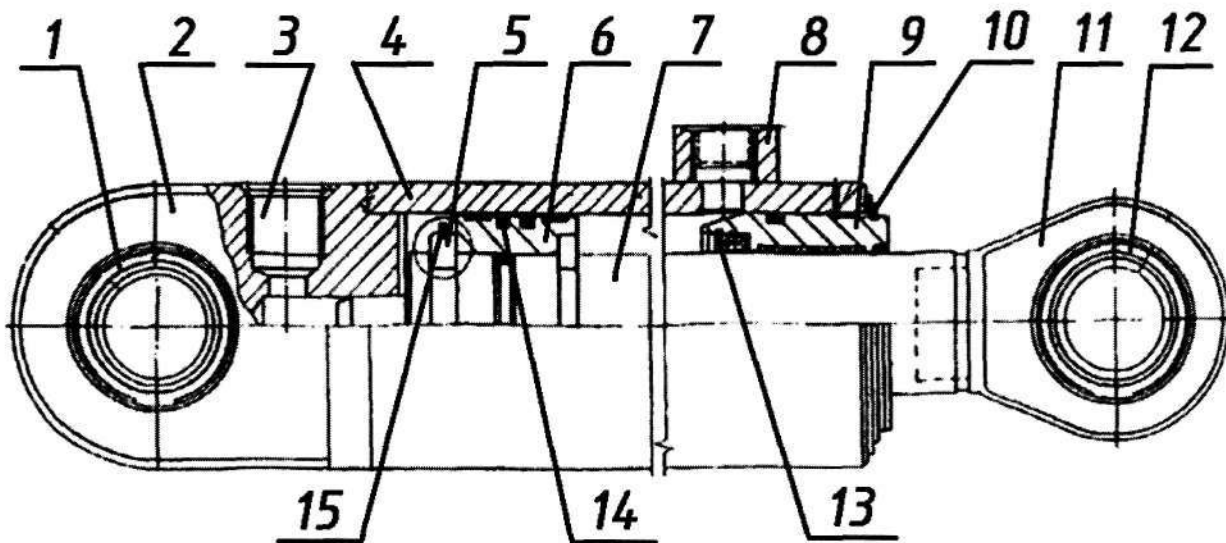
Общий вид типового поршневого гидроцилиндра
